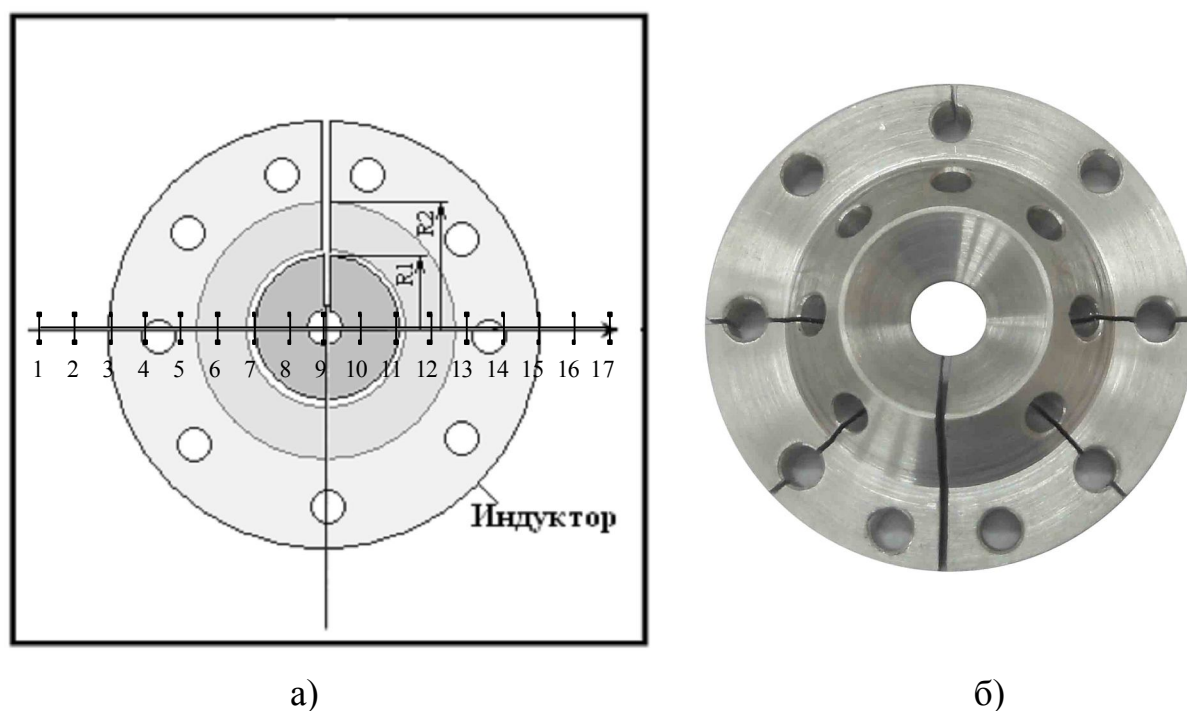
Индуктор с рабочей областью конического профиля: а) схематическое изображение; б) экспериментальный образец
